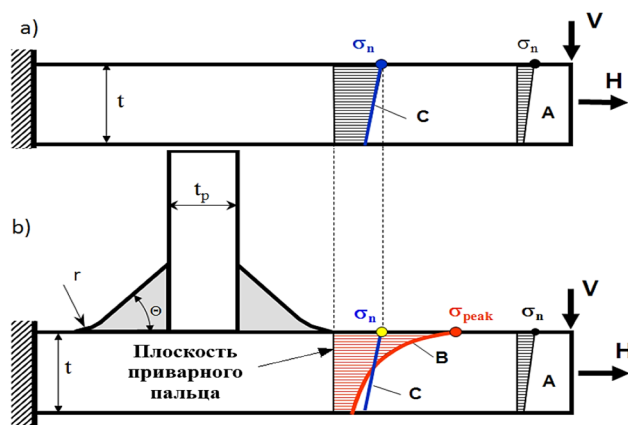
Напряжения в несварной и сварной пластинах, подвергнутых идентичным внешним системам нагружения а) поля напряжений в несварной пластине; б) поля напряжений в пластине с ненагруженным одностронним креплением, соединенным галтельными швами
